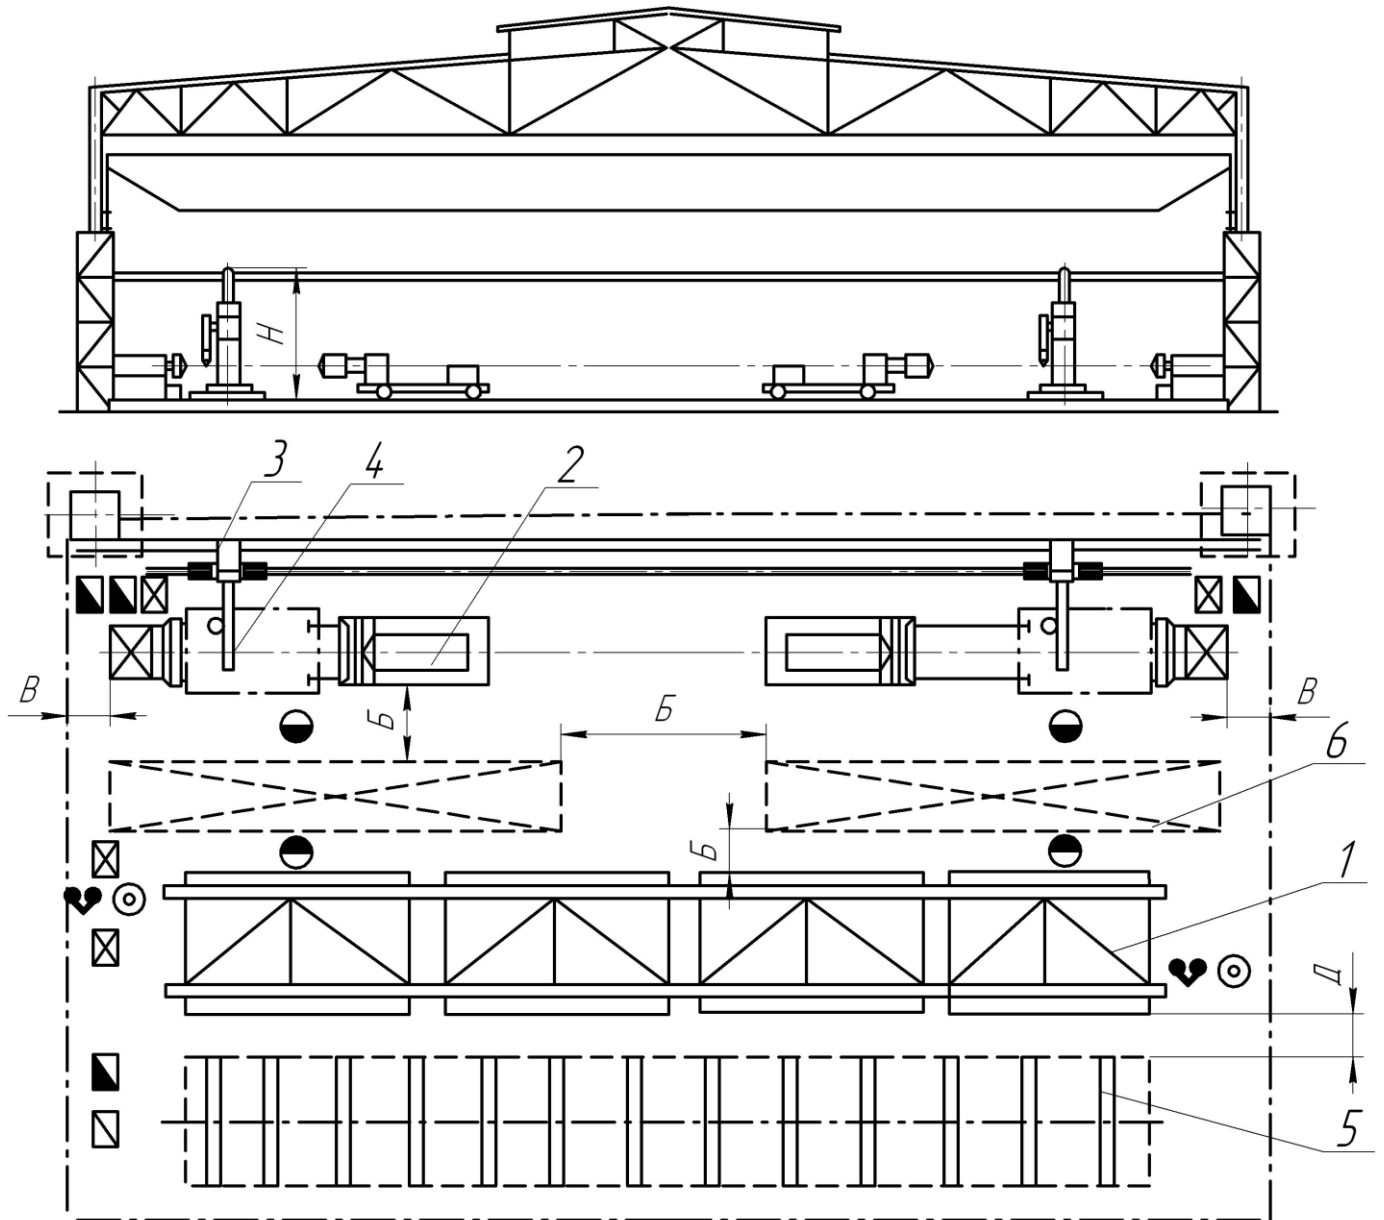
Схемы тележек для сварочных аппаратов:
